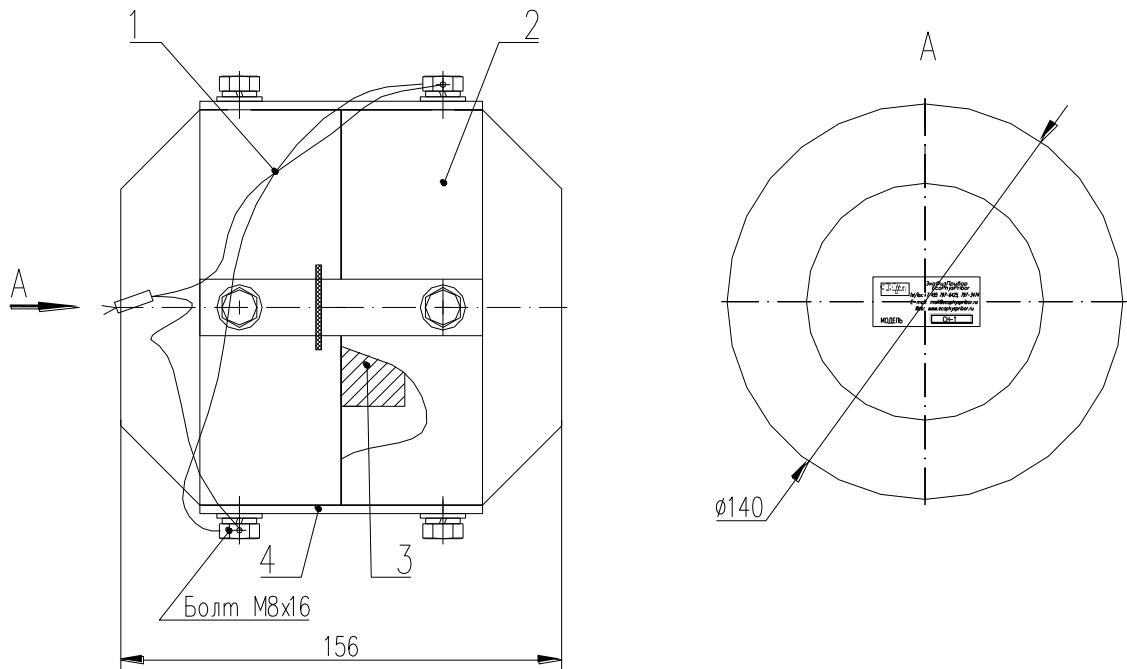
1 - кассета; 2 – транспортная заглушка; 3 - вкладыш; 4 – планка
